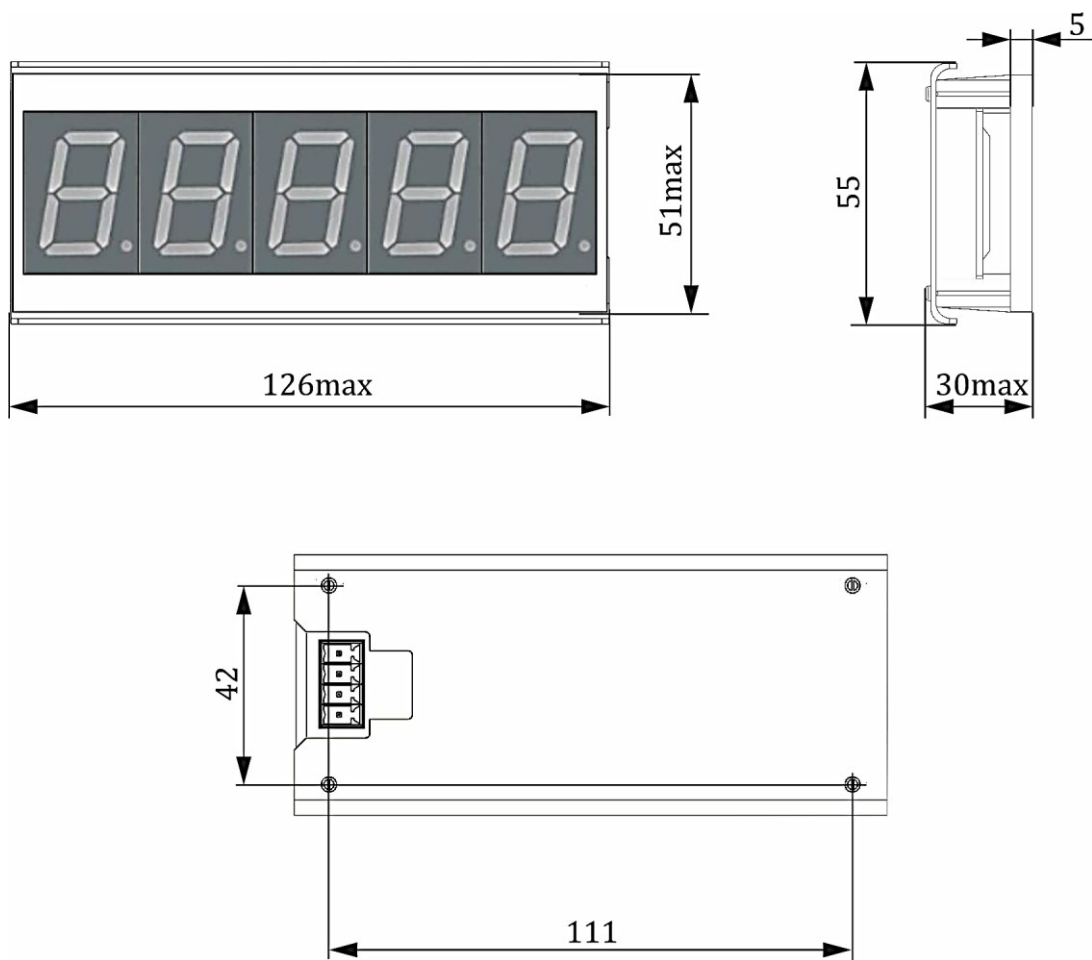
Габаритные и установочные размеры внешнего однострочного показывающего устройства E8DU 25
